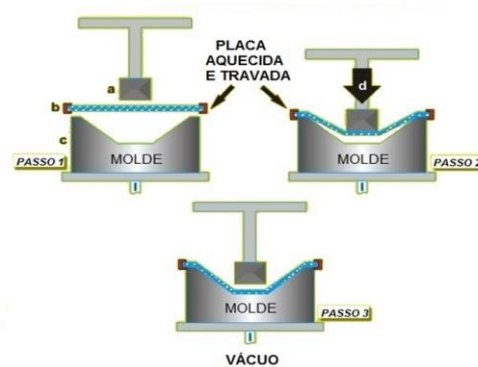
Termoformagem processo *billow snap-back vacuum forming
